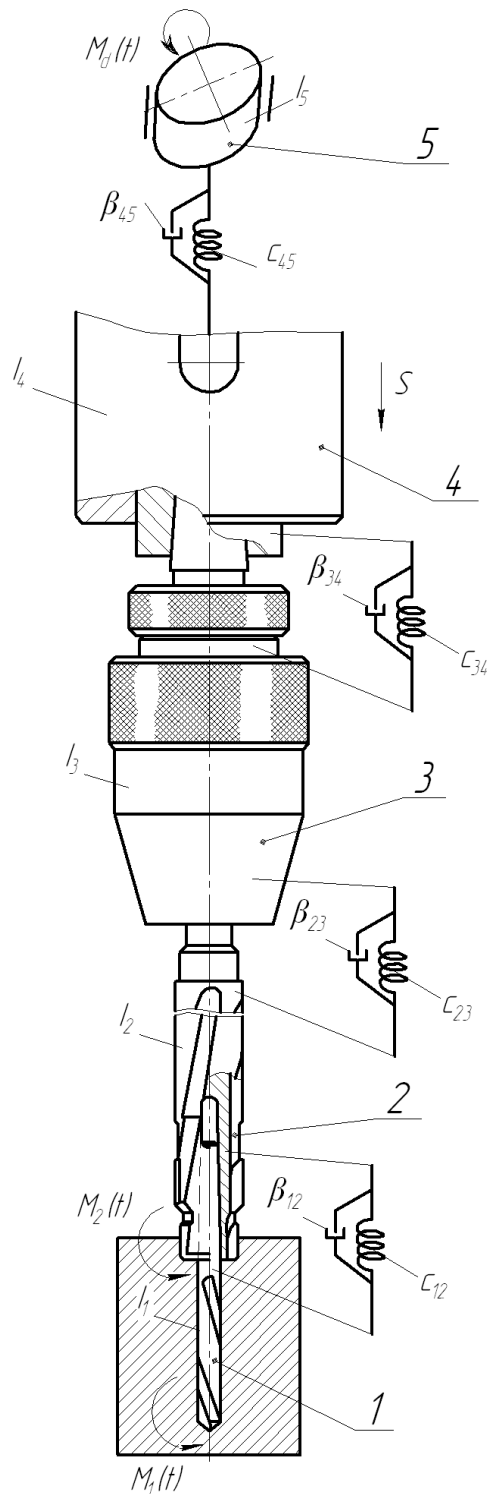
Розрахункова схема для динаміки системи комбінований інструмент (свердло-зенкер)-патрон-шпиндель-ротор двигуна для оброблення ступінчастого отвору: 1 – свердло, 2 – зенкер, 3 – патрон, 4 – шпиндель, 5 – ротор двигуна
